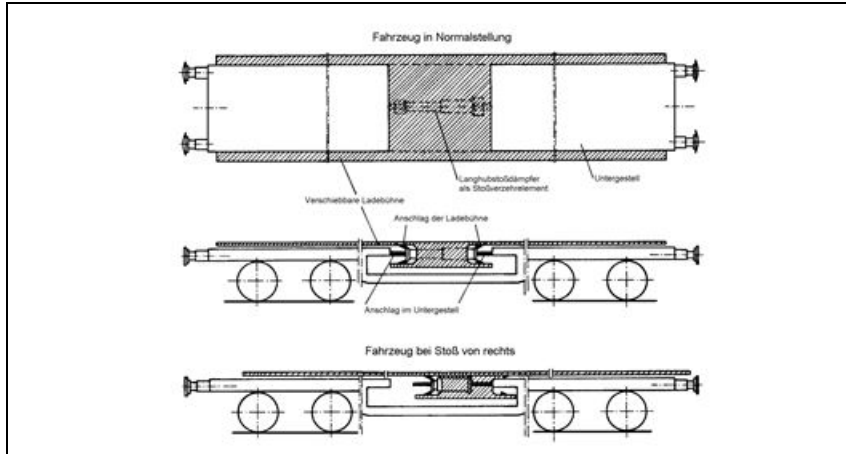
Langhubstoßdämpfer Prinzip verschiebbare Ladebühne
